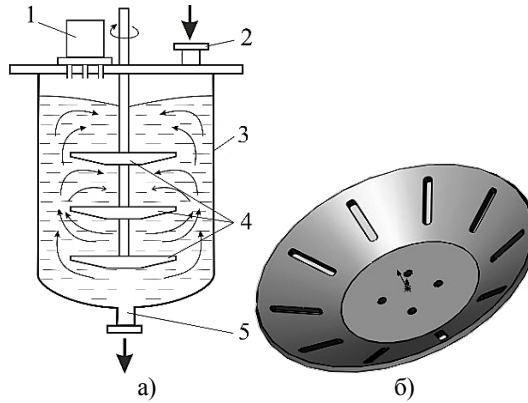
Схема змішувача напівфабрикатів: а) 1 — циліндрична камера; 2 — робочі органи; 3 — подача рідких компонентів; 4 — дозатор борошна; б) — робочий орган
